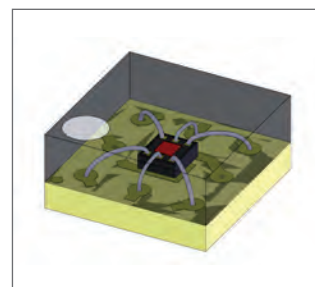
Ein Blick ins Innenleben der neuen Gehäuse-Familie
